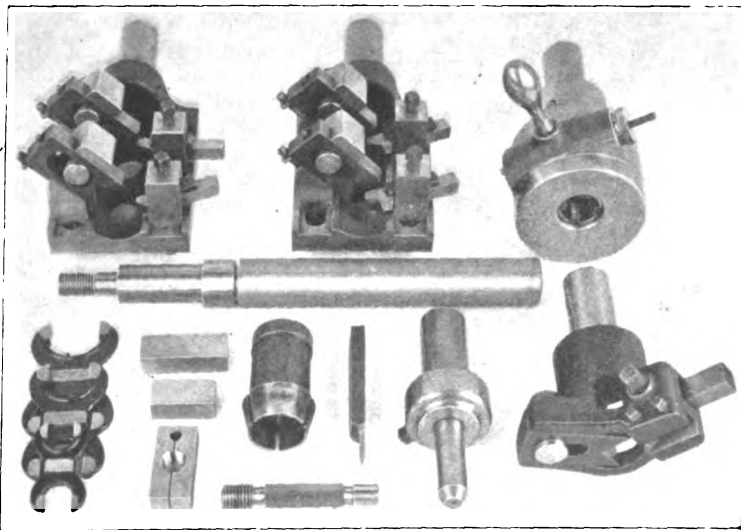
Werkzeug für die selbsttätige Revolverdrehbank.
